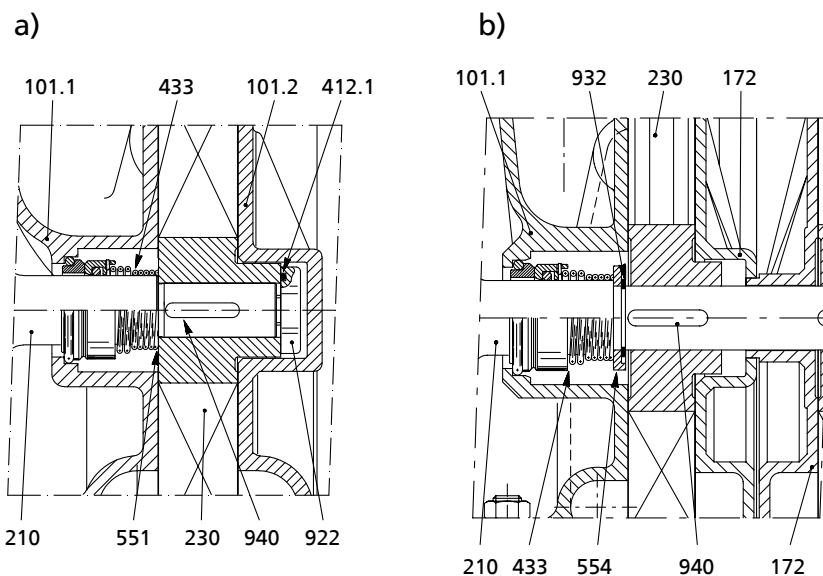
Ausführung Gleitringdichtung T, Fahrweise B
